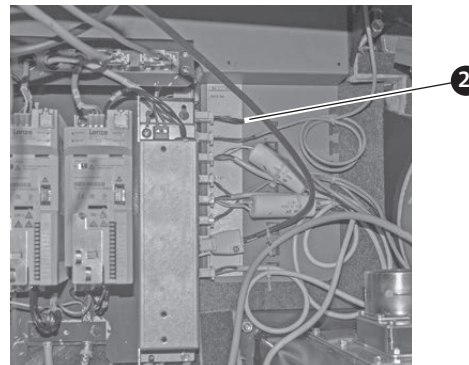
Stecker mit Brücke bei SRAS 230V anstecken
